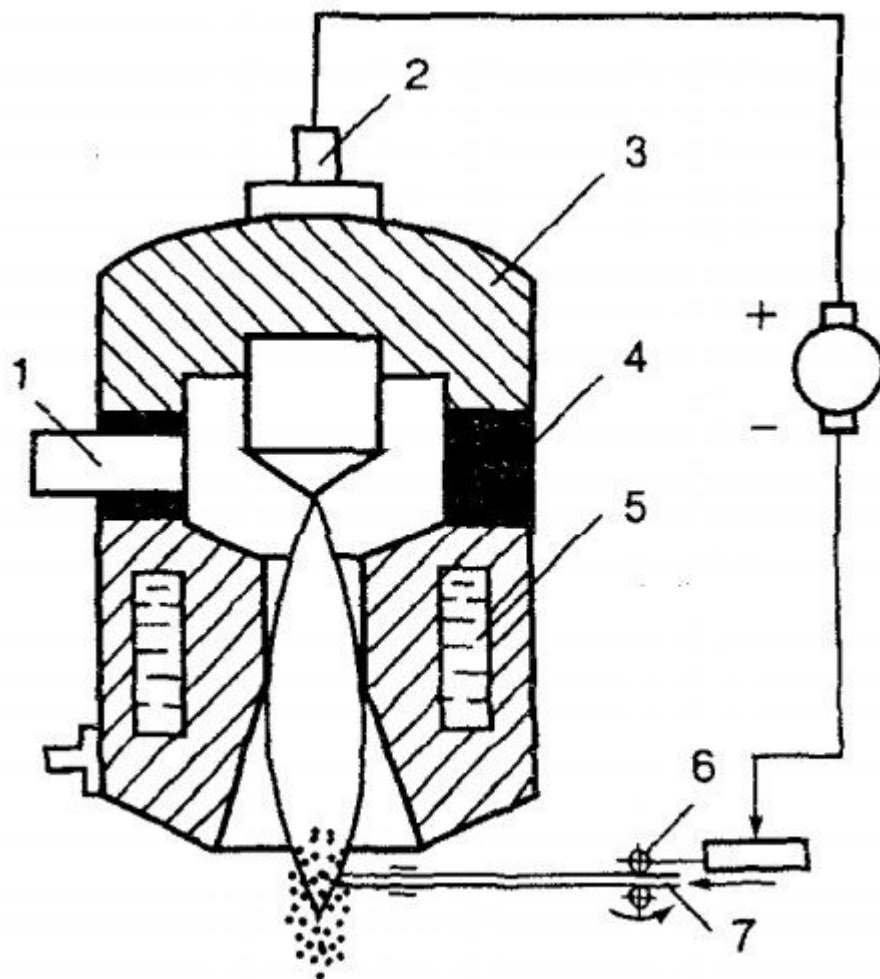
Принципиальная схема плазменного напыления с применением проволоки: 1 - подвод плазмообразующего газа, 2 - катод плазмотрона, 3 - корпус катода, 4 - изолятор, 5 - корпус анода, 6 - механизм подачи проволоки, 7 - сплошная или порошковая проволока, 8 - плазменная дуга, 9 - источник питания.
